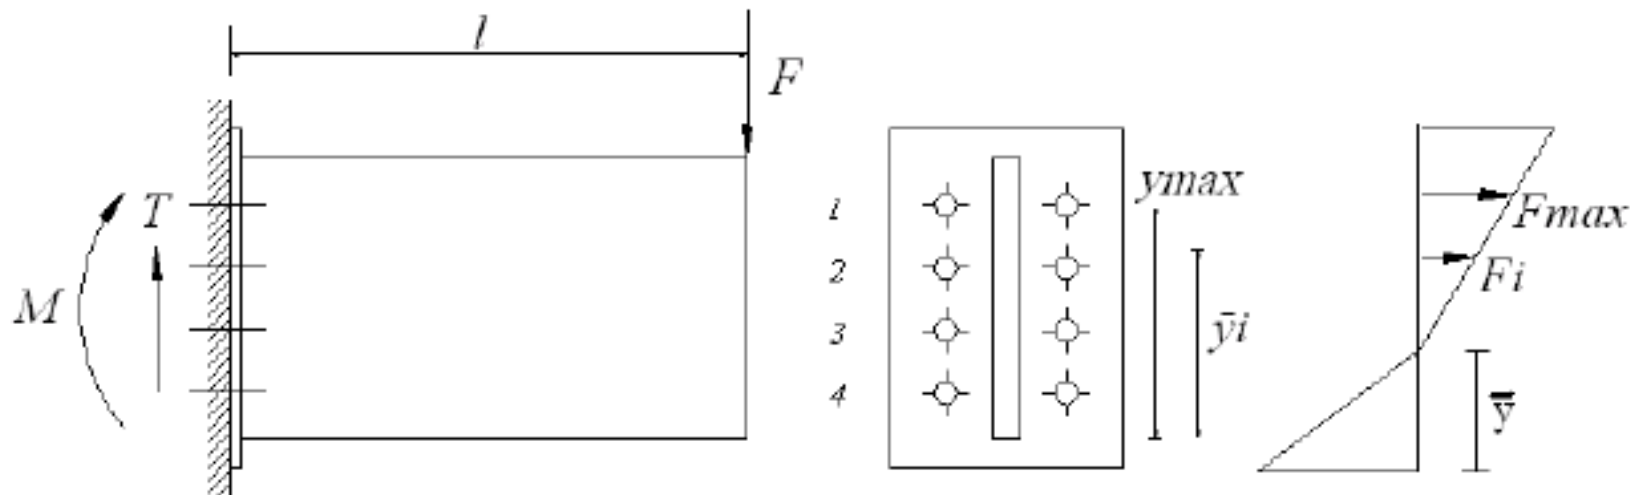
Flangia con zona compressa di dimensioni finite.
